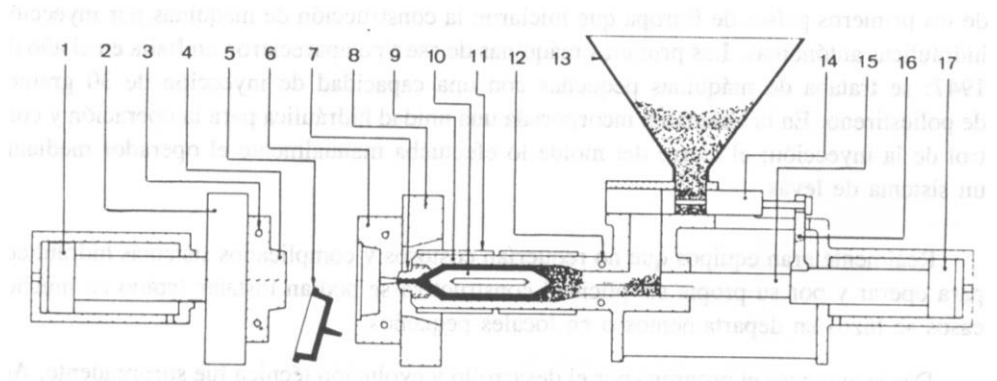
Diagrama de una máquina de moldeo por inyección tipo pistón. Todos los componentes móviles de la máquina están representados al finalizar el ciclo. Nótese que la pieza moldeada (5) es expulsada del molde-1. Pistón de cierre del molde-2. Platina móvil-3.- Circuito de agua para el enfriamiento del molde-4. Medio molde móvil -5. Pieza moldeada.-6. Medio molde fijo-7. Boquilla -8. Platina fija-9. Cilindro de plastificación-10. Torpedo-11. Resistencia eléctrica para calentamiento del cilindro de plastificación-12. Circuito de agua para el enfriamiento del cilindro de plastificación-13. Tolva-14. Dosificador-15. Pistón de inyección-16. Brazo que actúa el dosificador-17. Pistón hidráulico e inyección.
